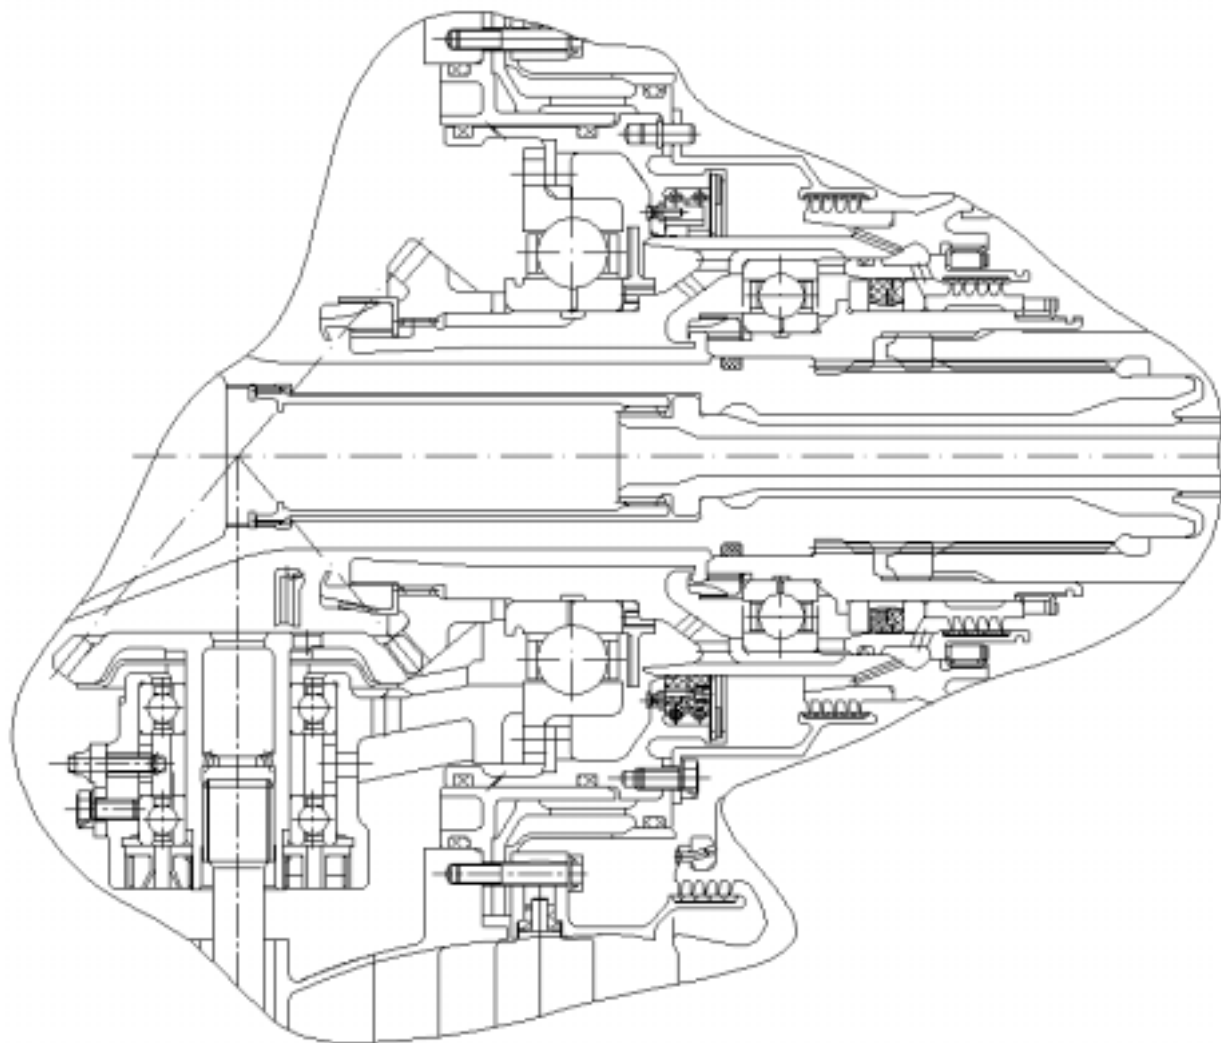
Конструкция передней опоры КВД с межвальным подшипником
